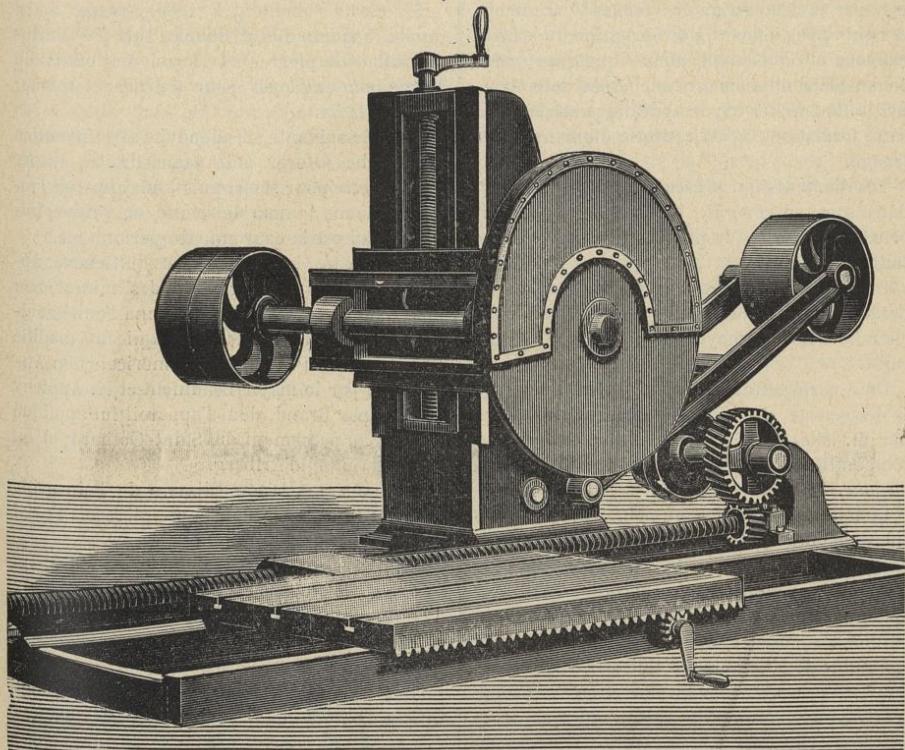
Outilage au diamant. — Machine à lame circulaire pour scier et moulurer.
